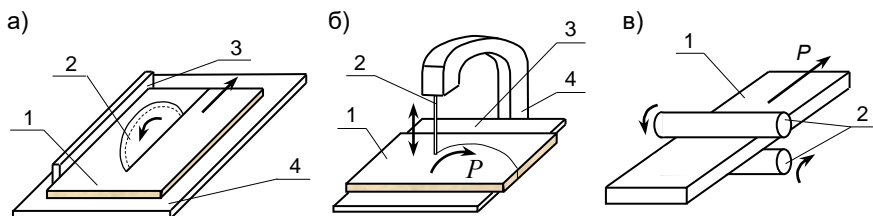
Схемы работы деревообрабатывающих станков:
